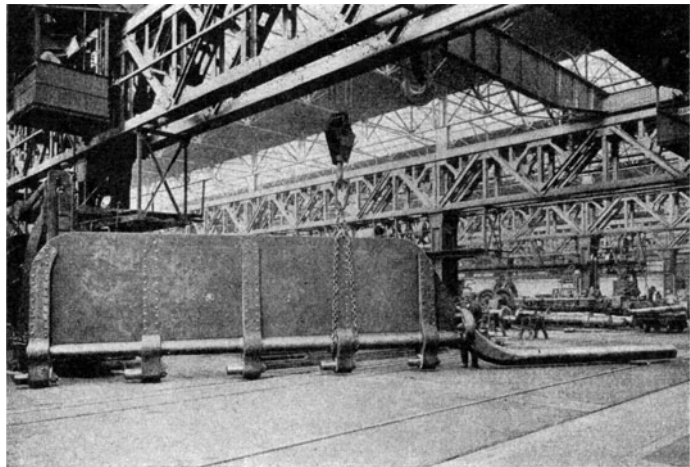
Komplettes geschmiedetes Ruder mit Beplattung.
